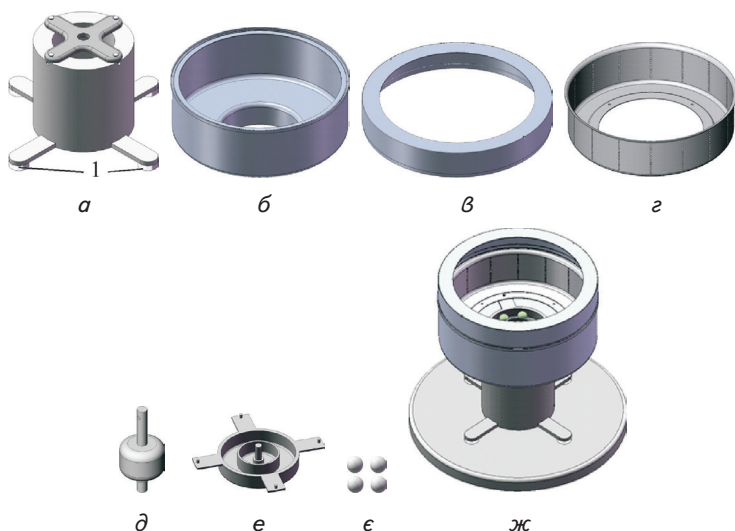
Комп'ютерні 3D-моделі основних вузлів і деталей модернізованої відцентрованої сокодавки та 3D-модель сокодавки в зібраному вигляді: а – корпус приводу; б, в – нижня і верхня кришка; з – сито; д – ротор; е – корпус автобалансира; е – кулі; ж – 3D-модель в зібраному вигляді; 1 – опори
